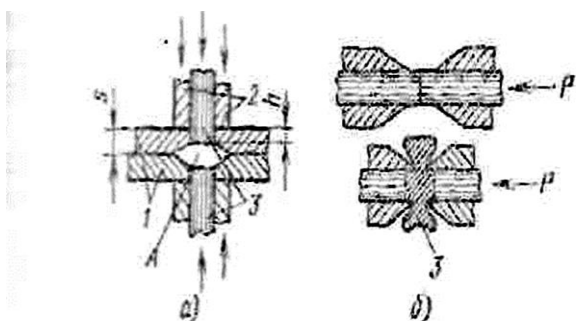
Схемы холодной сварки: а-точечная, б-стыковая,
